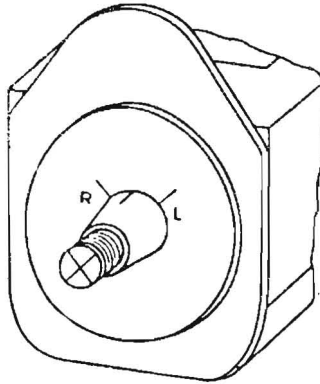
Richtiges Einstellen der Einspritzpumpe zum Motor
